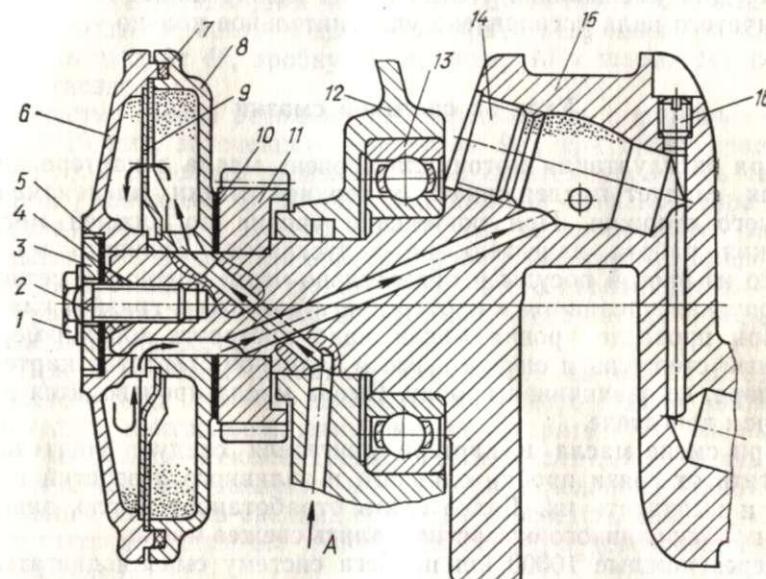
Центрифуга и передний коренной шарикоподшипник:
